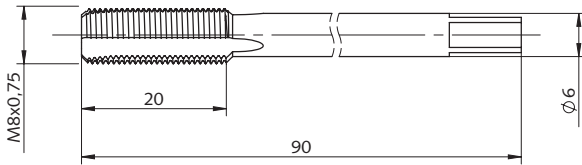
Gewindebohrer M8x0,75 Typ 1361
